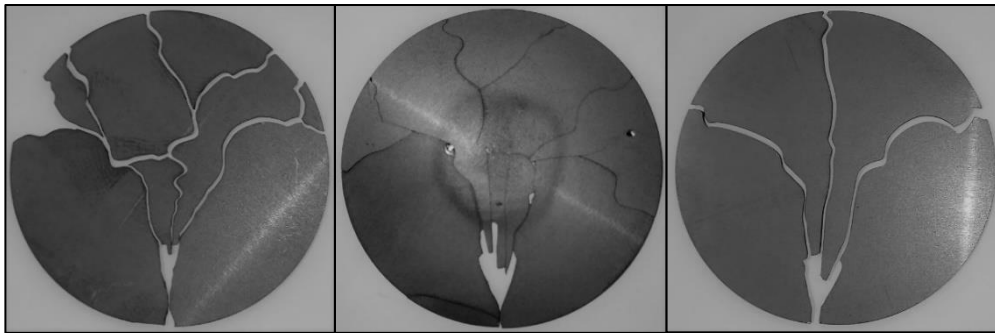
Immagini dischi in carburo di silicio rotti per le prove di resistenza del materiale.
